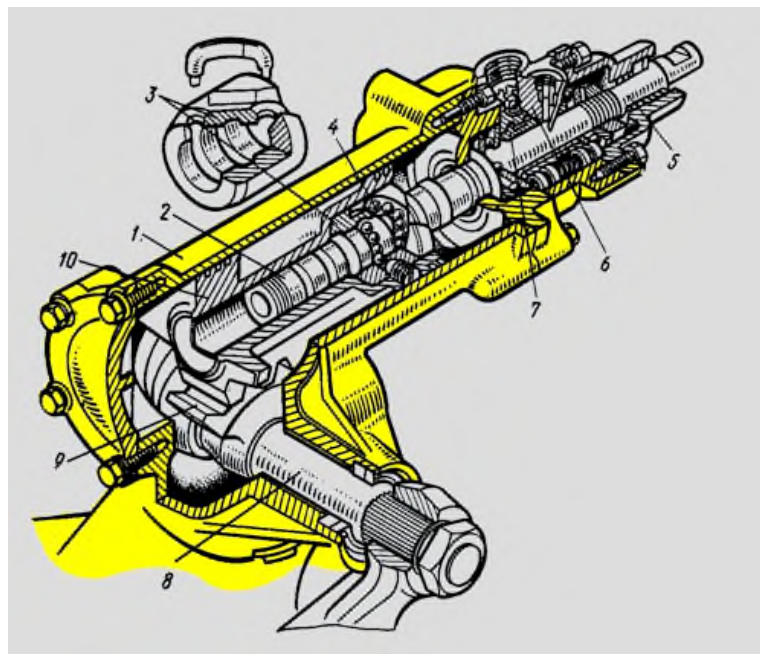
Устройство рулевого механизма с встроенным гидроусилителем
